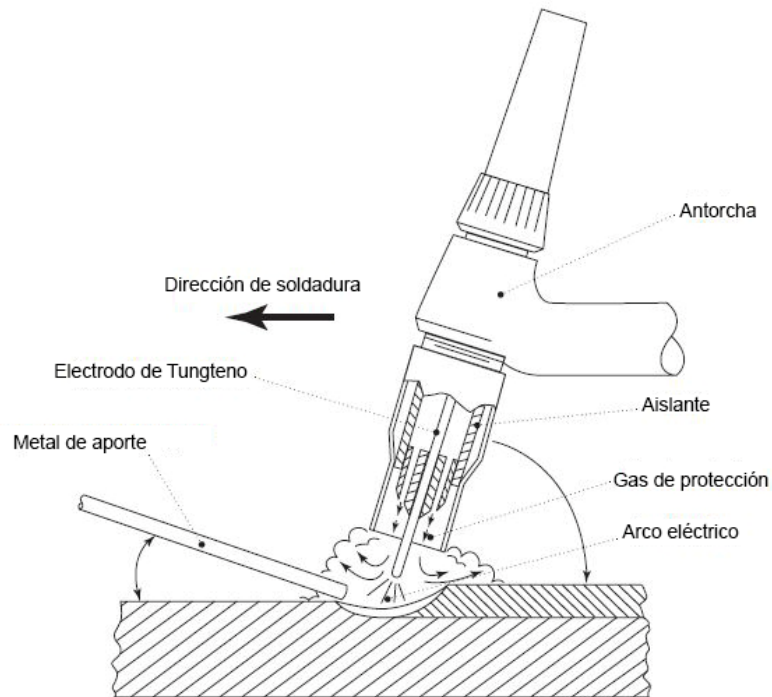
Soldador utilizando técnica GTAW (TIG), haciendo unión con material de aporte. Elaboración propia®
